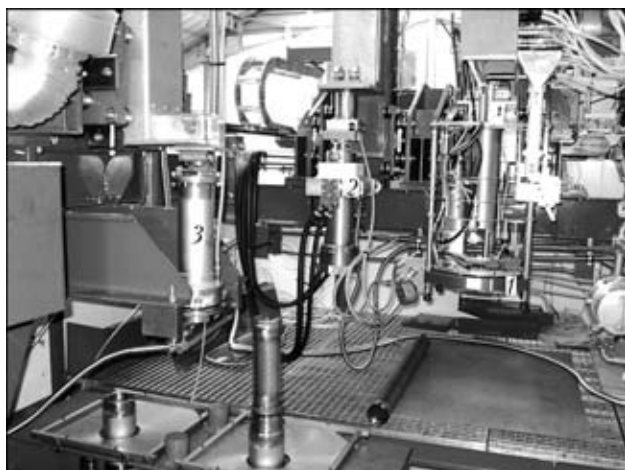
Общий вид специальной установки для приварки колпака с патроном П-89 в камере: 1 — головка для приварки колпака к патрону; 2 — головка для закачки гелия и приварки герметизации (сварки) отвода штуцера; 3 — головка для контроля патрона на непроницаемость гелием после полного цикла работ по герметизации
